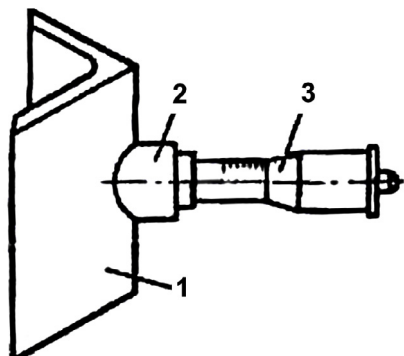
Приспособление для измерения расстояния от поверхности вала до струны:
